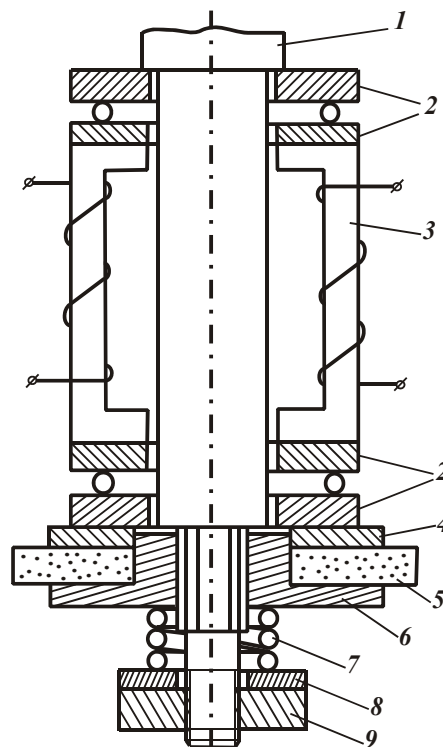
Вращающийся магнестрикционный вибратор с неподвижным преобразователем: 1 – вал, передающий вращение на круг, со шлицами и резьбой на конце; 2 – упорные шариковые подшипники; 3 – магнестрикционный преобразователь; 4 – шайба; 5 – круг; 6 – шлицевая втулка, на которую устанавливается круг; 7 – пружина; 8 – шайба; 9 – гайка.
